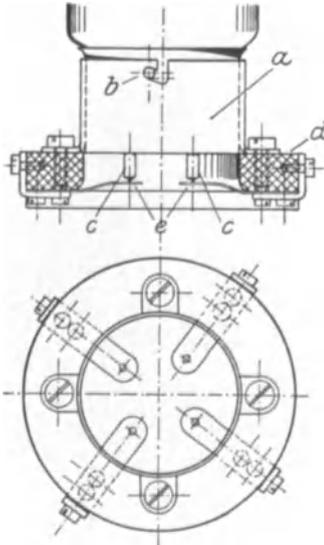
Sockel mit Swan-Fassung für Röhren.
